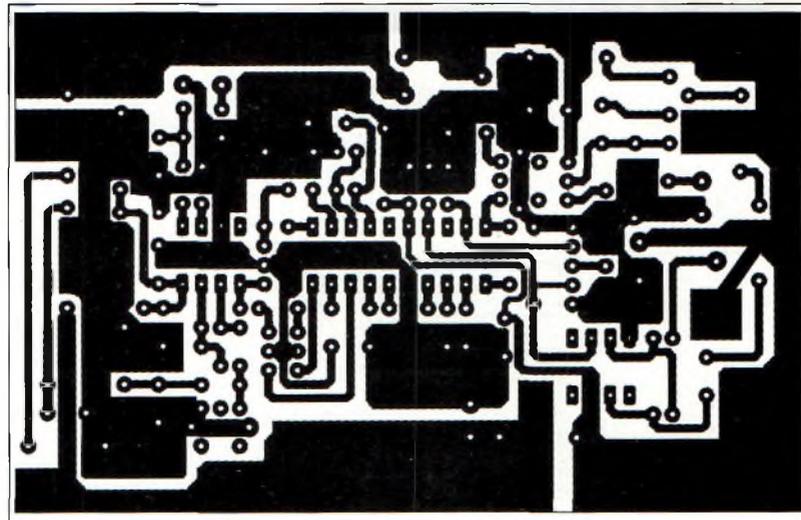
Le dessin du circuit imprimé à l'échelle 1 sur 1, vu du côté des pistes (soudures).
